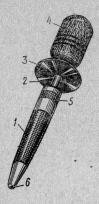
1— корпус; 2— шток; 3— ограничитель; 4— ручка; 5— гайка; 6— ловитель
